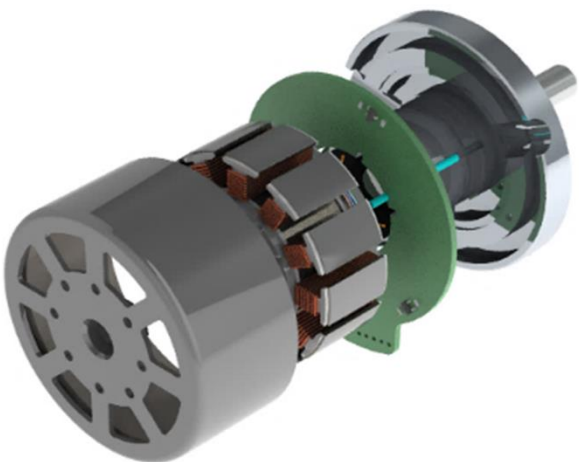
3D-Explosionszeichnung eines Motors mit offenem Nutenrotor.
